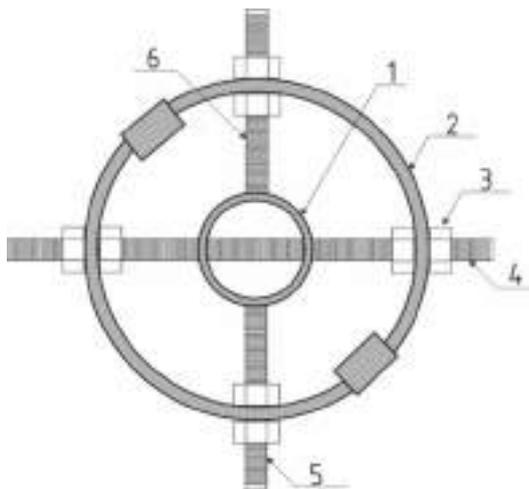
Схема переходной соединительной головки для станка для навязки пожарных рукавов
